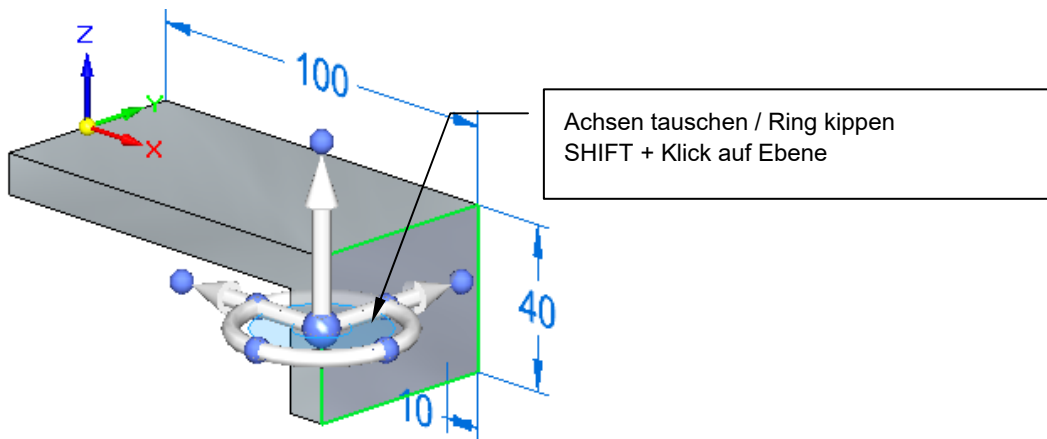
Steuerrad in der Ebene frei verschieben
